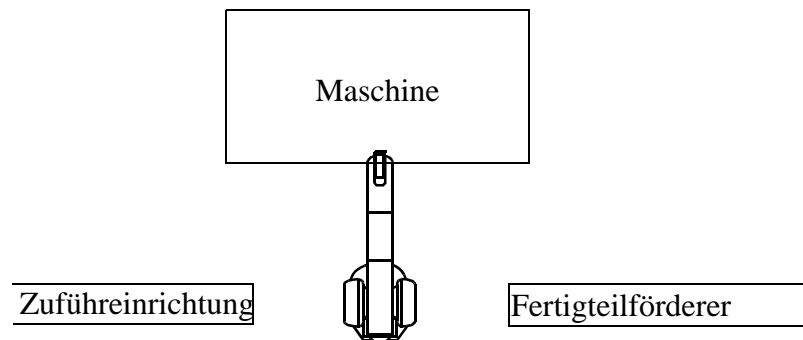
Der Manipulator legt ein Werkstück in die Maschine ein, das anschließend bearbeitet wird.
